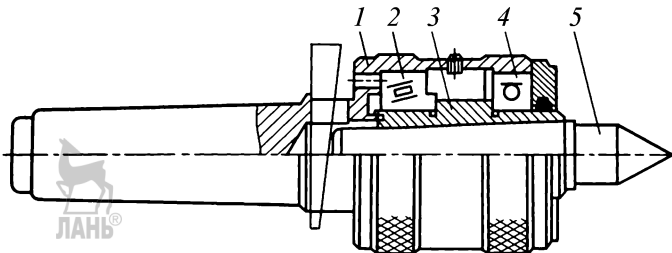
Универсальный корпус для съемных вращающихся центров:
